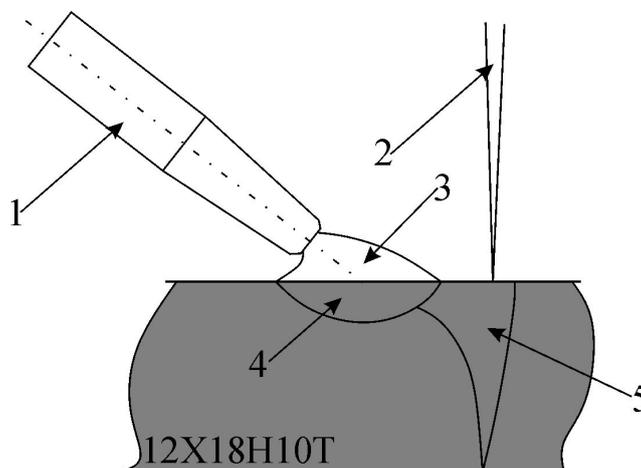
Схема процесса гибридной лазерной сварки
